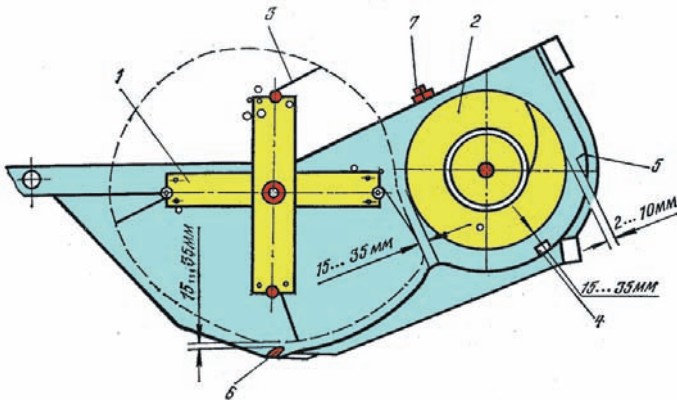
Регулировка мотовила и шнека жатки для уборки трав комбайном КПИ-2,4: 1 — мотовило; 2 — шнек; 3 — зуб пружинный; 4, 5 — чистики; 6 — палец; 7 — болт установочный.
